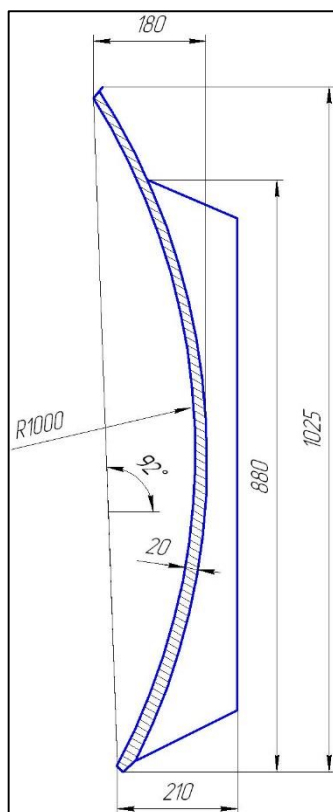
Схема отвальной поверхности с основными габаритными размерами
